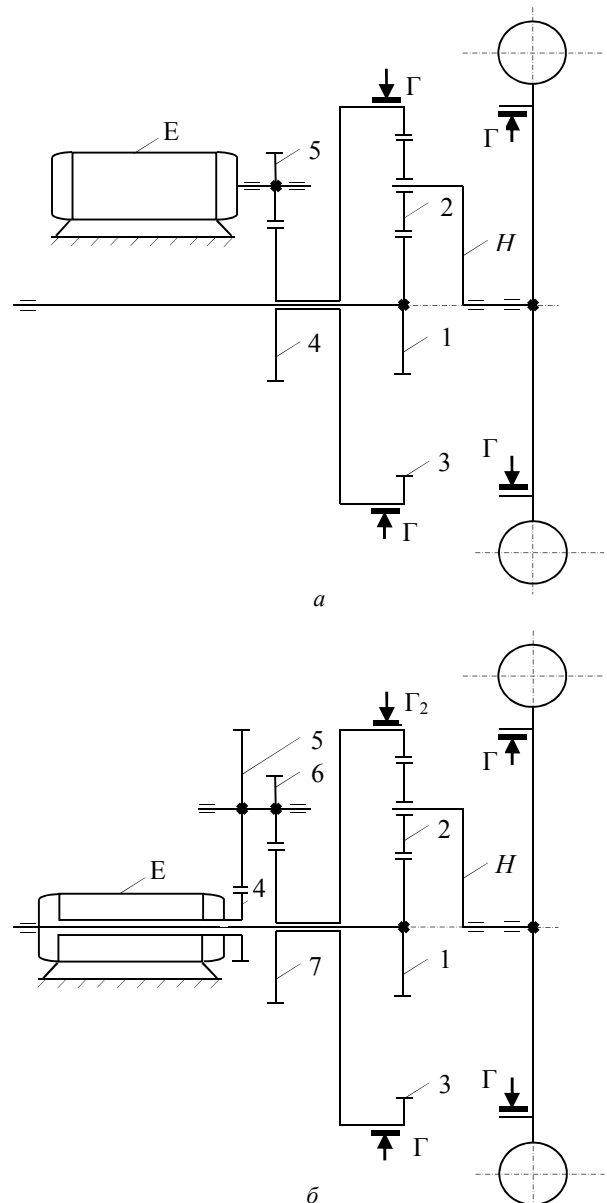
Схема гібридного електромеханічного приводу ведучого колеса автомобіля:
